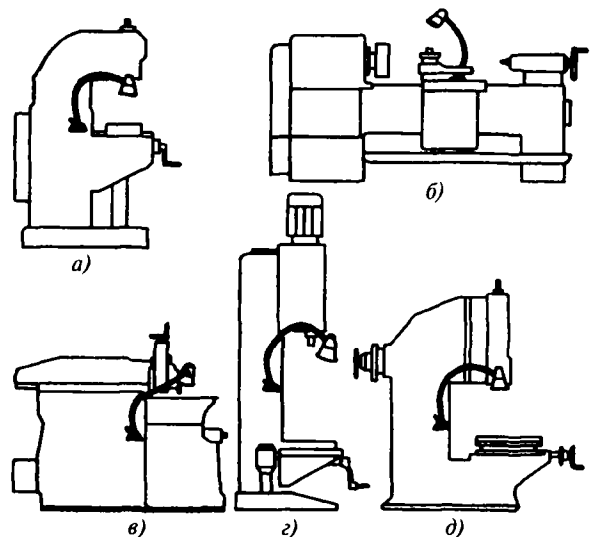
Схема установки ОП местного освещения на металлообрабатывающих станках: а — вертикально-фрезерном; б — токарном; в — поперечно-строгальном; г — сверлильном; д — долбежном
